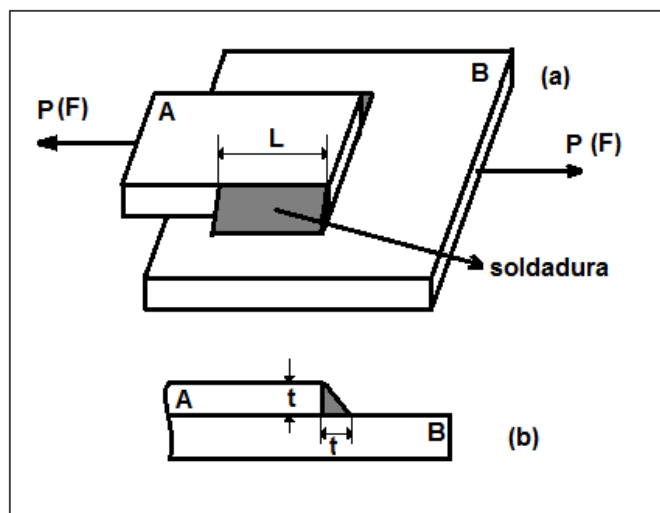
Unión soldada traslapada con cargas concéntricas
